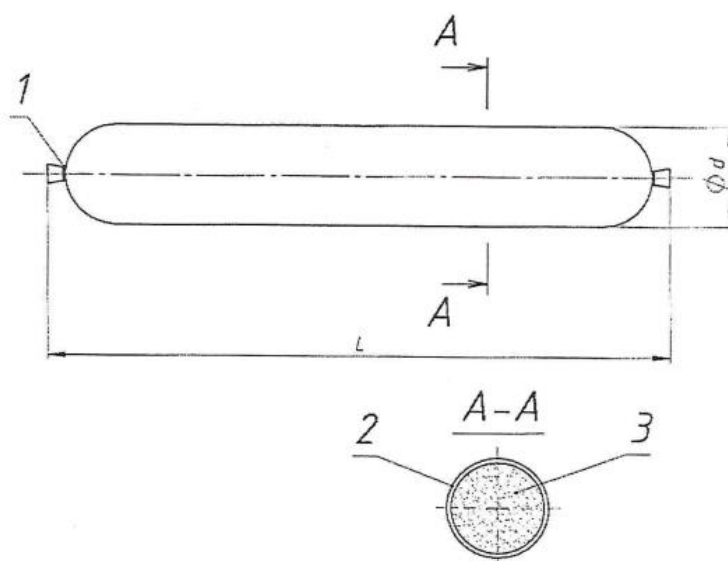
Конструкция и основные параметры патрона «Гидронит - П».
